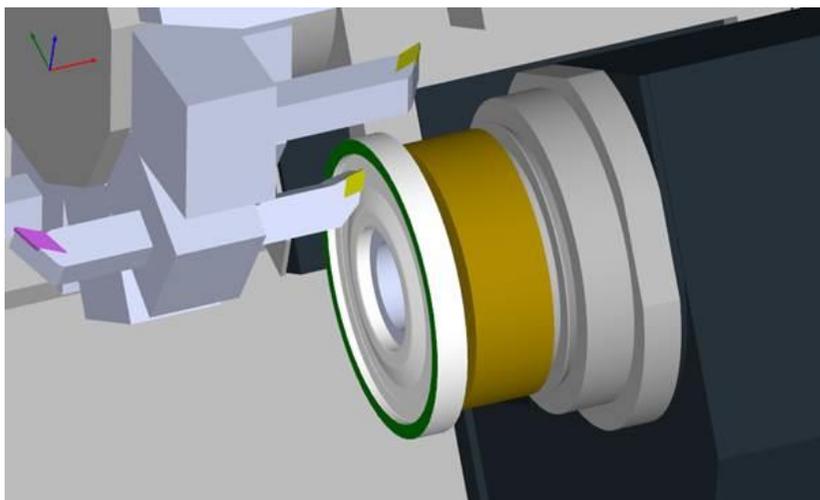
Процесс точения левой стороны диска компрессора ГТД
